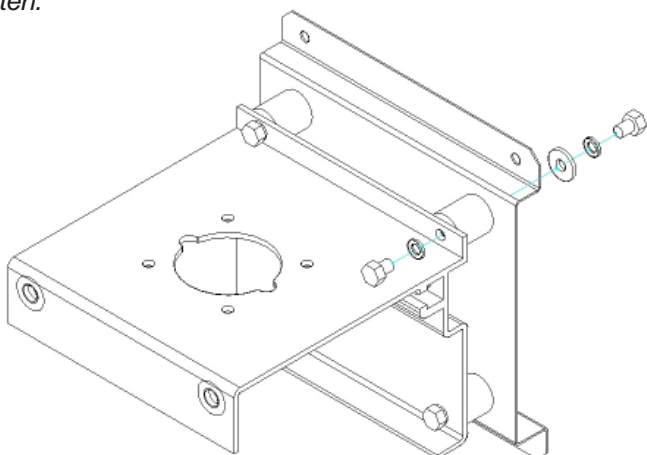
Befestigung der Halterung an der Wand mit 4 Stück 5x16 Schrauben.
